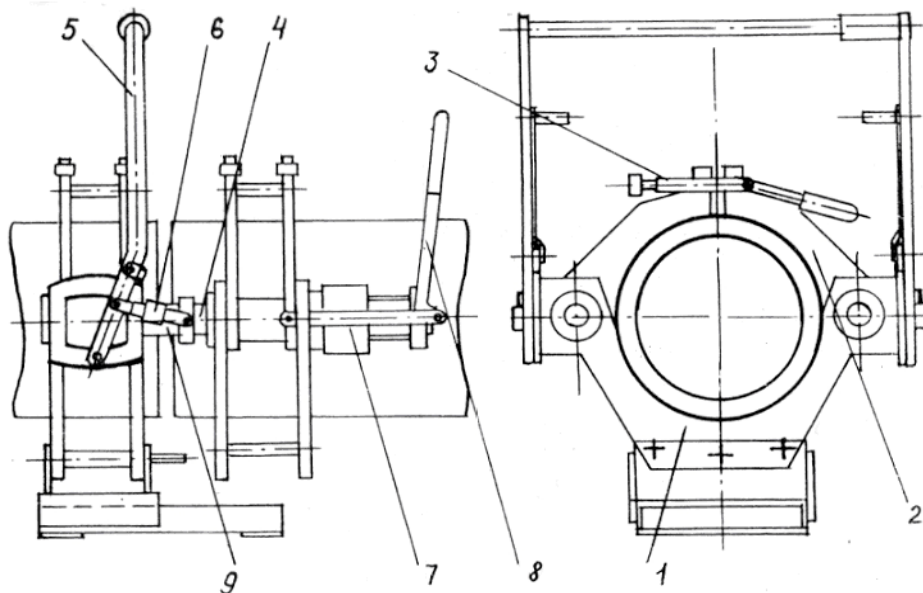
Монтажний пристрій для зварювання пластмасових труб  $D_H$  140...225мм УСПМ-225:
